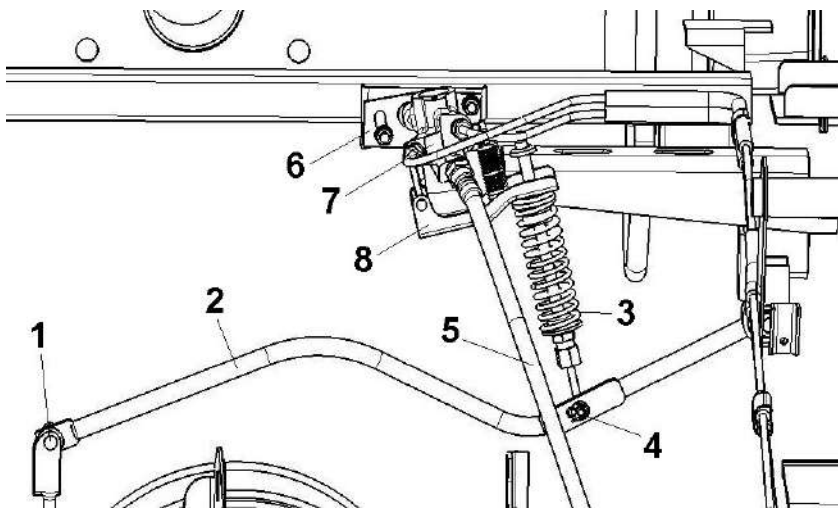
Привод регулятора давления: 1- палец крепления штанги привода регулятора; 2- штанга; 3- пружина привода в сборе с тягой; 4- шплинт; 5- задний тормозной шланг; 6- кронштейн крепления регулятора; 7- регулятор; 8- рычаг привода регулятора
